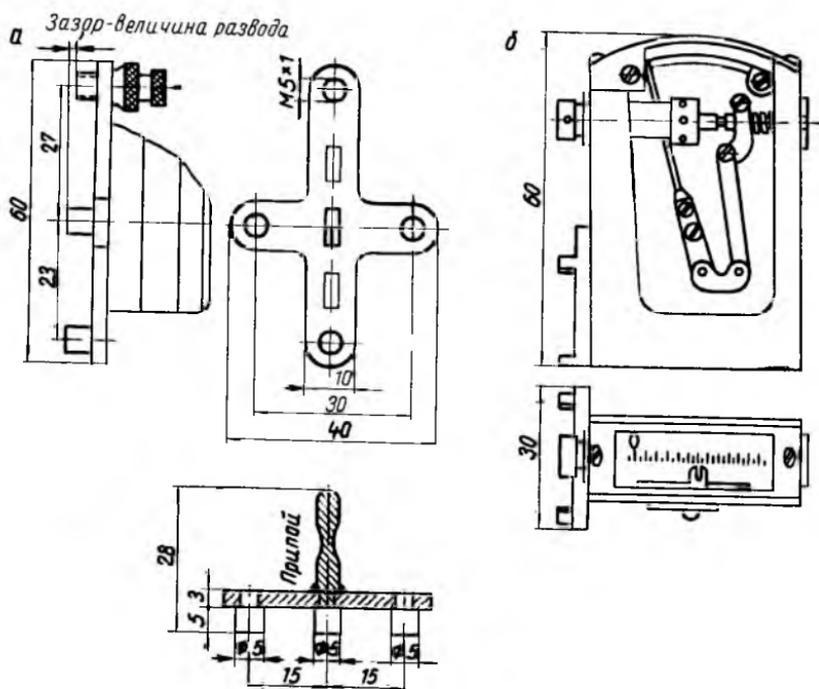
Шаблоны и контрольный прибор для проверки развода зубьев:
